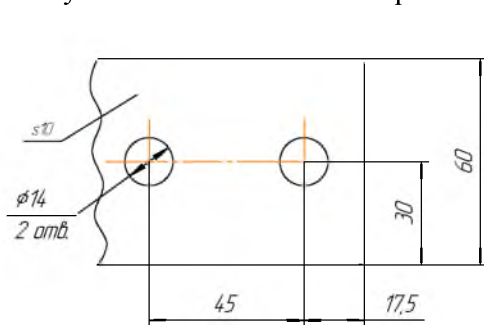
Разметка отверстий для присоединения подводящих проводов для РГП СЭЦ® -110/1250
